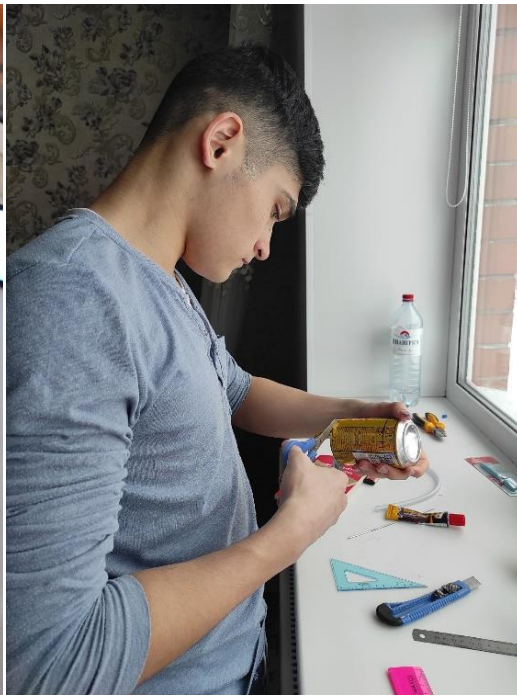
,17 Изготовление коленчатого вала и махового колеса
